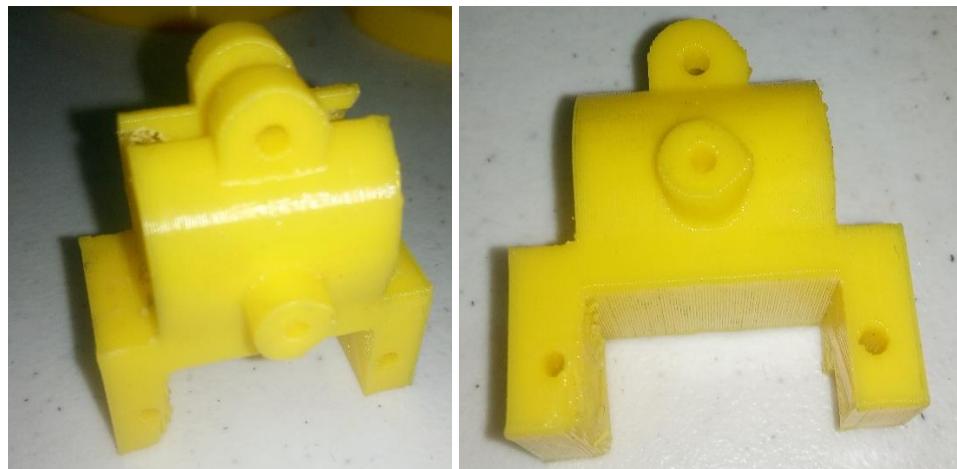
Impresión del modelado en 3D del bloque de rodamiento lineal.
